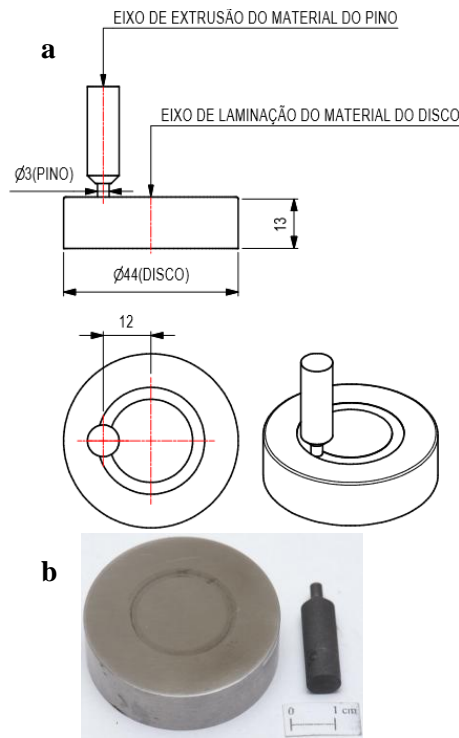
a) Dimensional (mm) dos pares, pino e disco, utilizados no ensaio, b) imagem de um disco e um pino pós usinagem.
